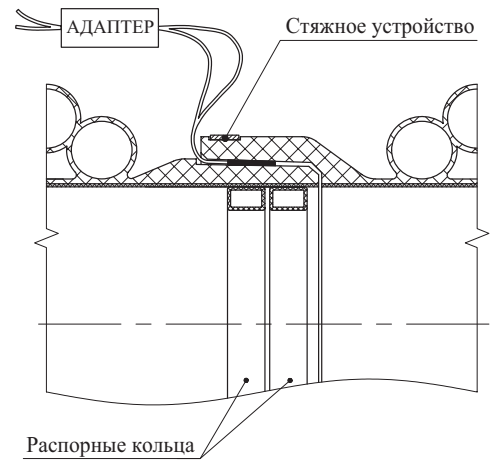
Схема сварки растробного соединения с закладными нагревателями
